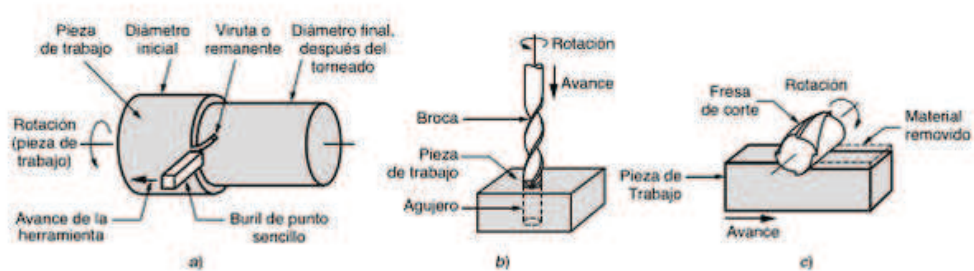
operaciones comunes de maquinado: a) Torneado b) Taladro c) Fresado
